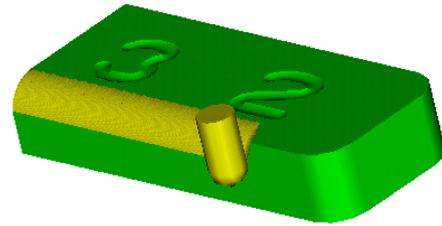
Bearbeitungssimulation eines Stempels für das Ziehwerkzeug mit einem Kugelfräser
